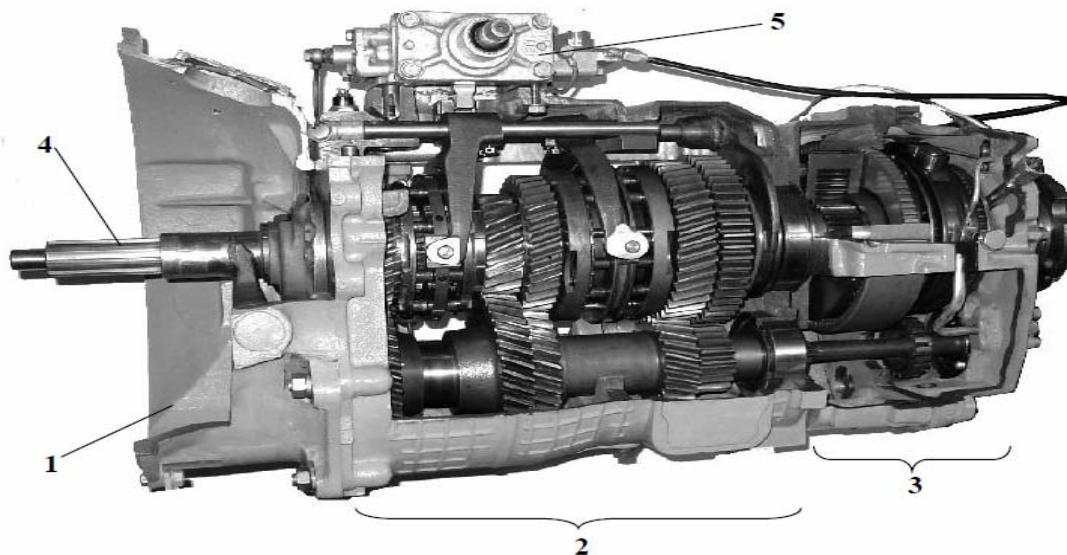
Конструкция восьмиступенчатой коробки передач КАМАЗ модели 161:
